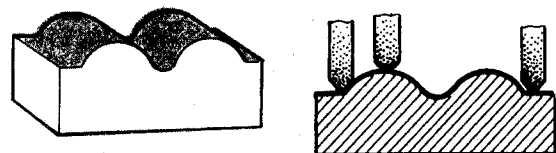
Схема эквидистантного шлифования профиля детали штампа
